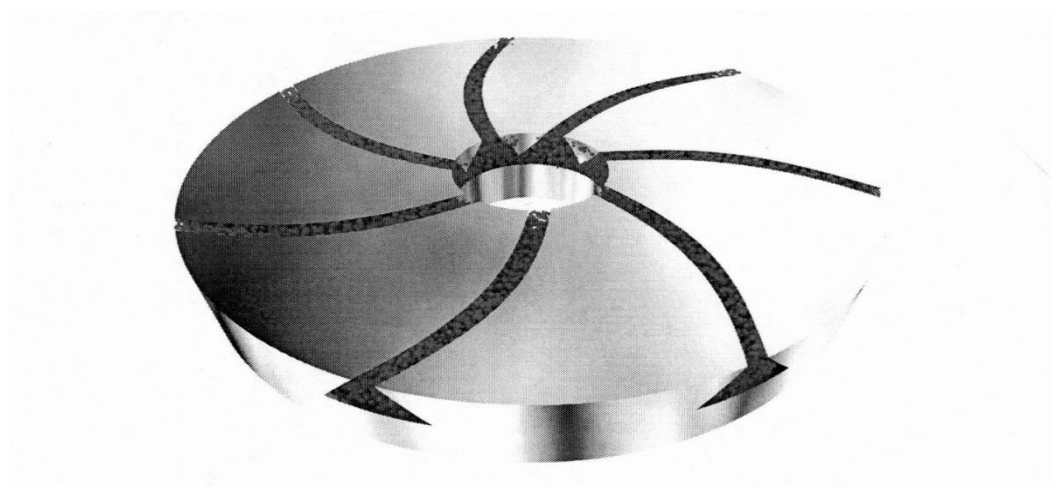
Общий вид композиционного шлифовального круга для обработки рабочей поверхности рельса
